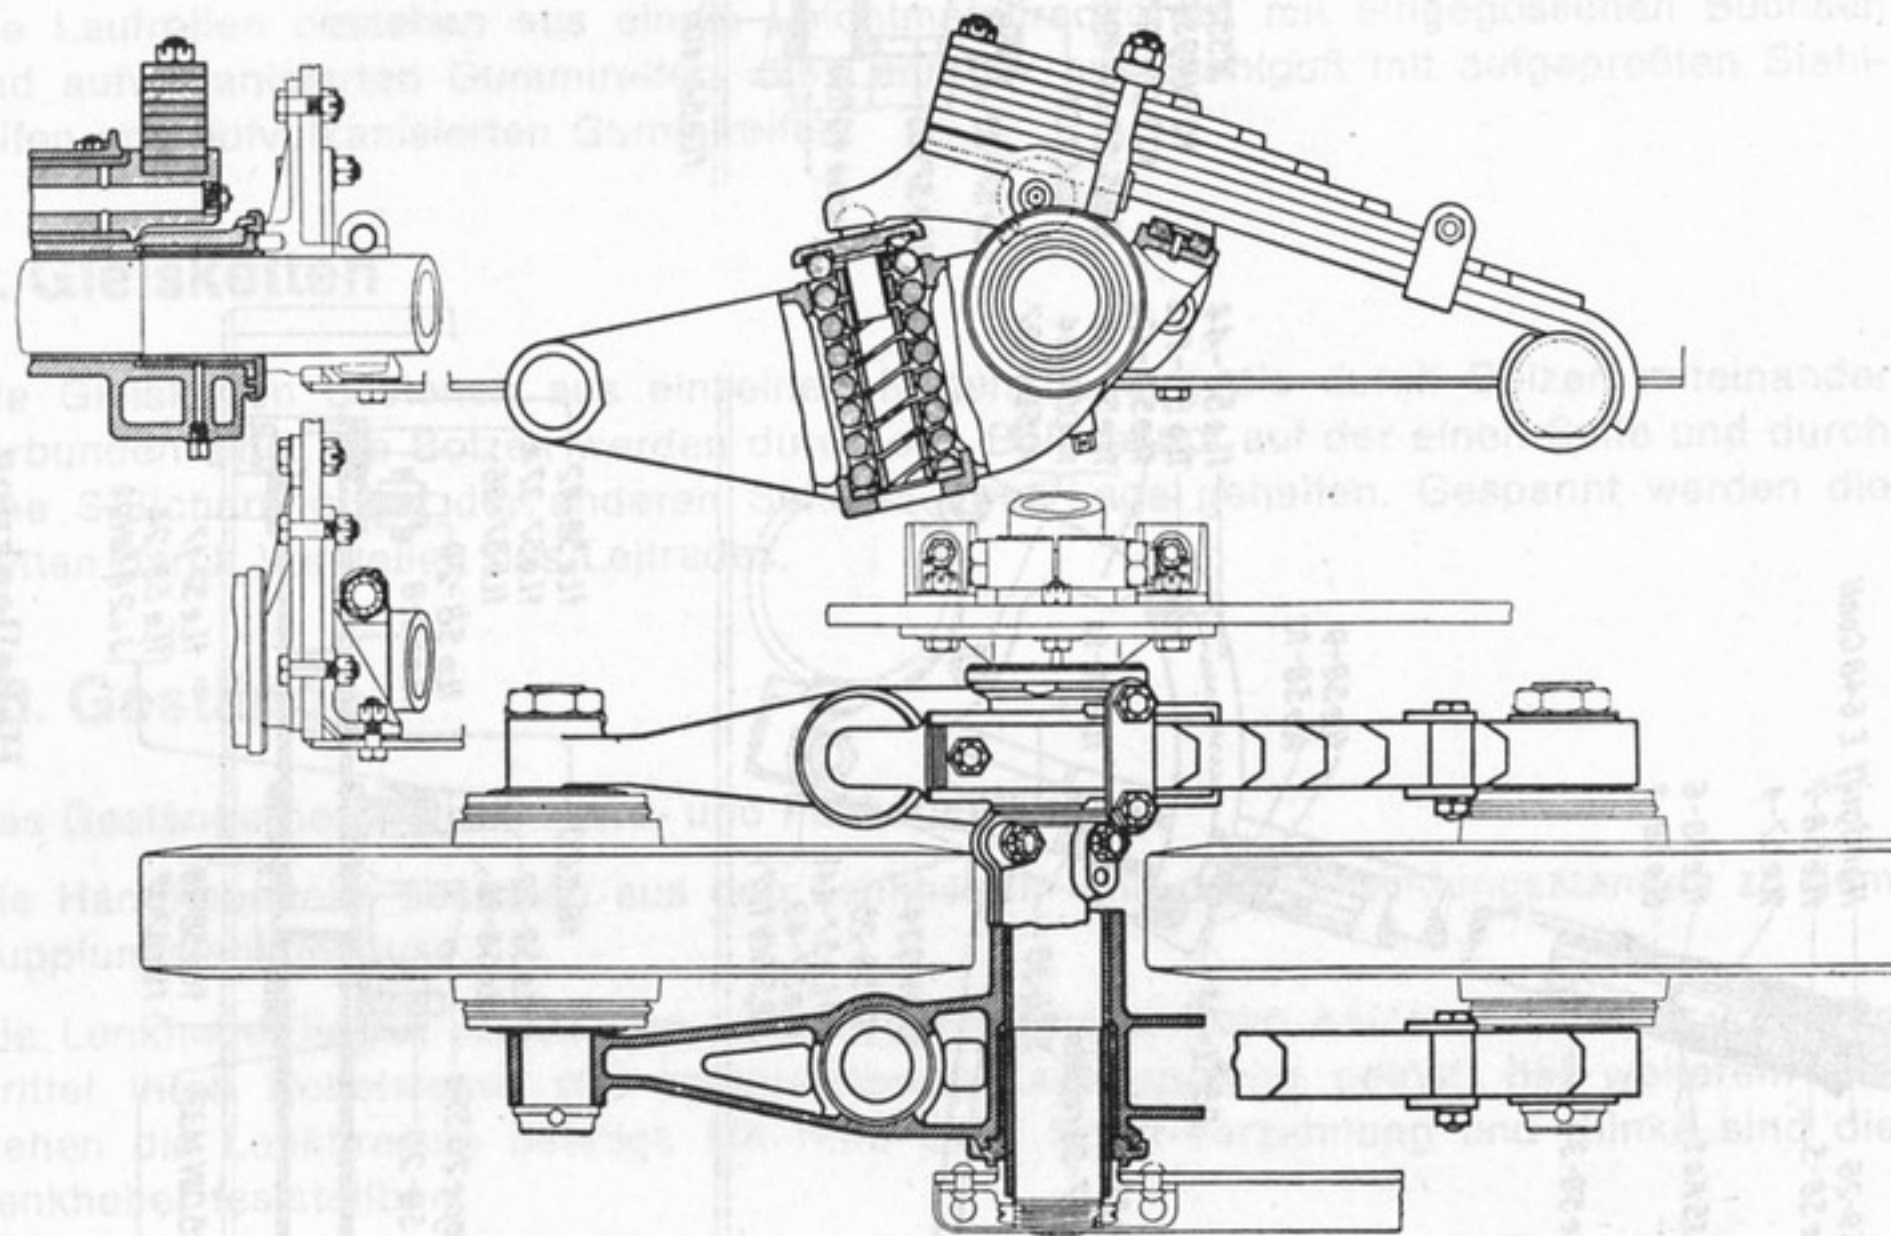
Mittlerer Laufwerkshebel (Schnitt)
